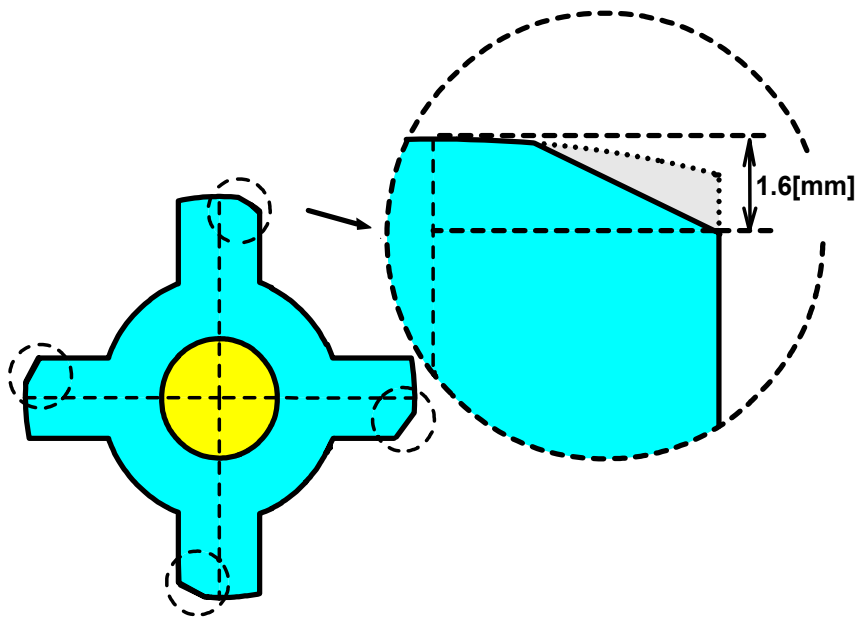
Rotor 극의 우측모서리 부분을 단절한 형상
